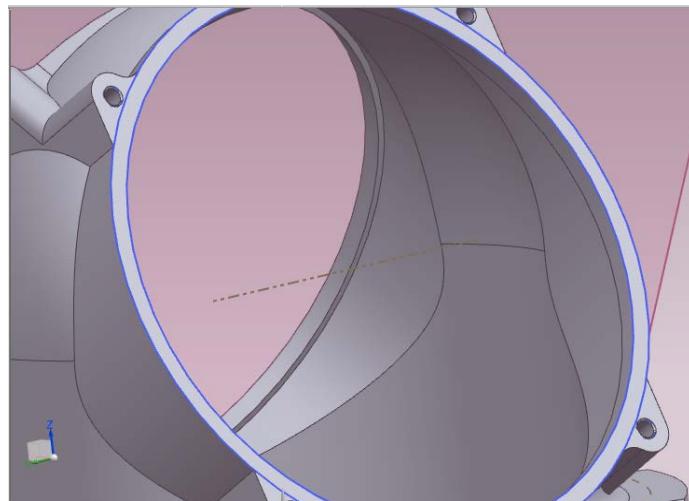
3D модель корпуса с окончательно построеными фланцевыми частями
